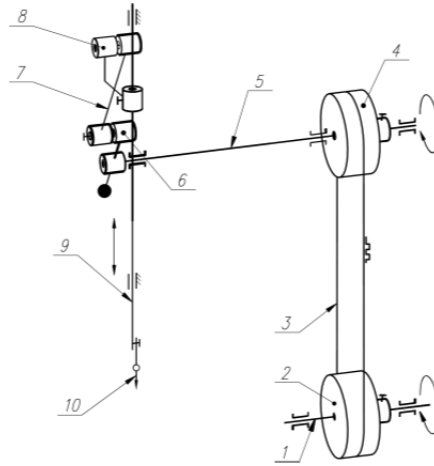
Схема механізму голки швейної машини для зашивання мішків
